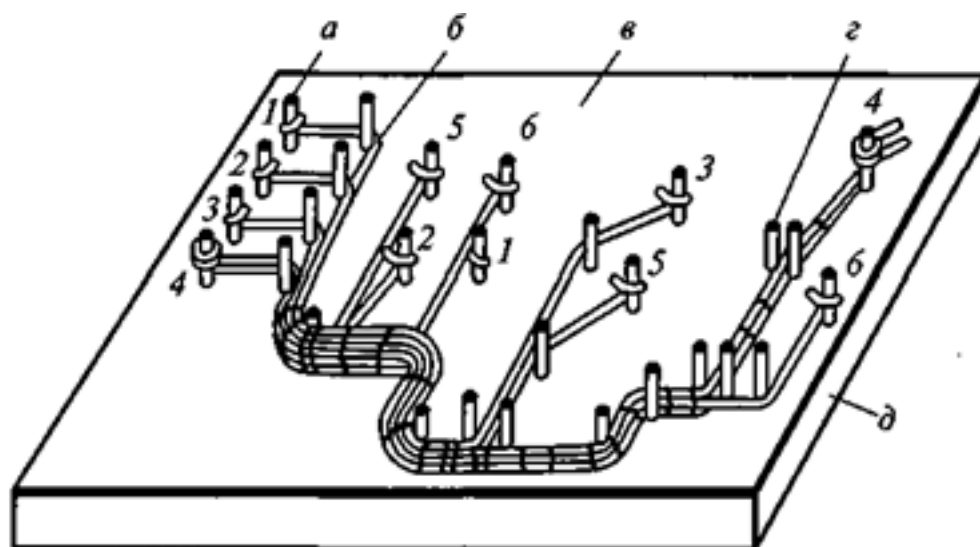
Шаблон для укладки и вязки жгутов:
